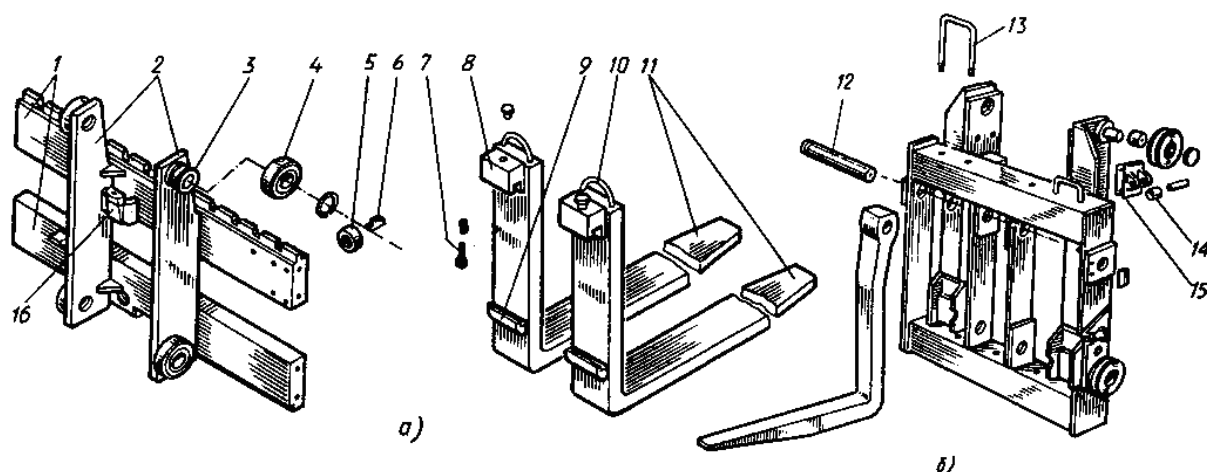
Каретки: а – с жестким креплением подхватов;
